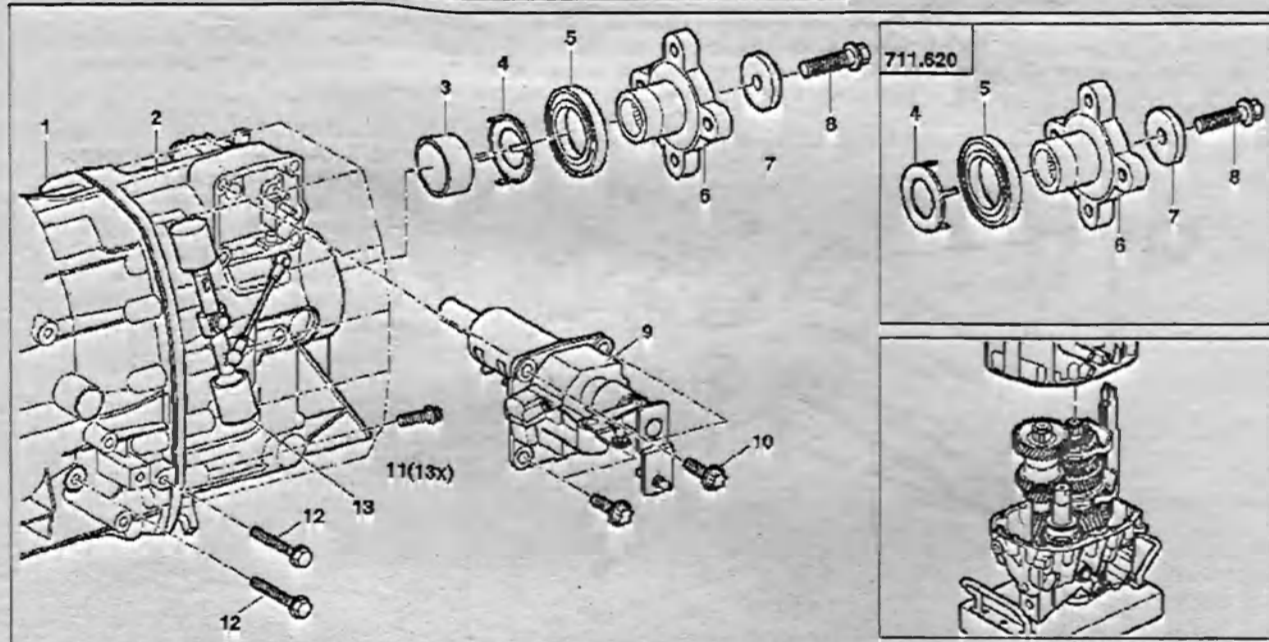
Разборка и сборка корпуса МКПП 711.605/620/621:
